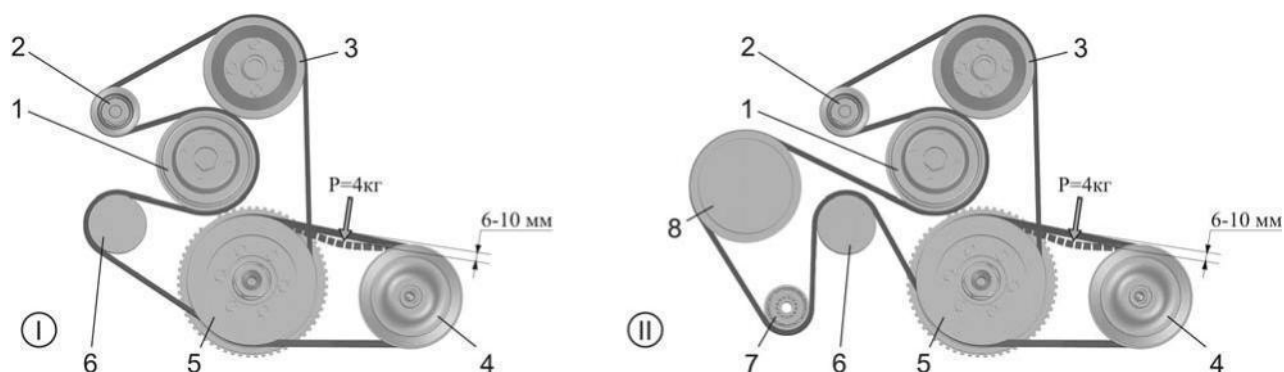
Схема натяжения ремней привода агрегатов:
